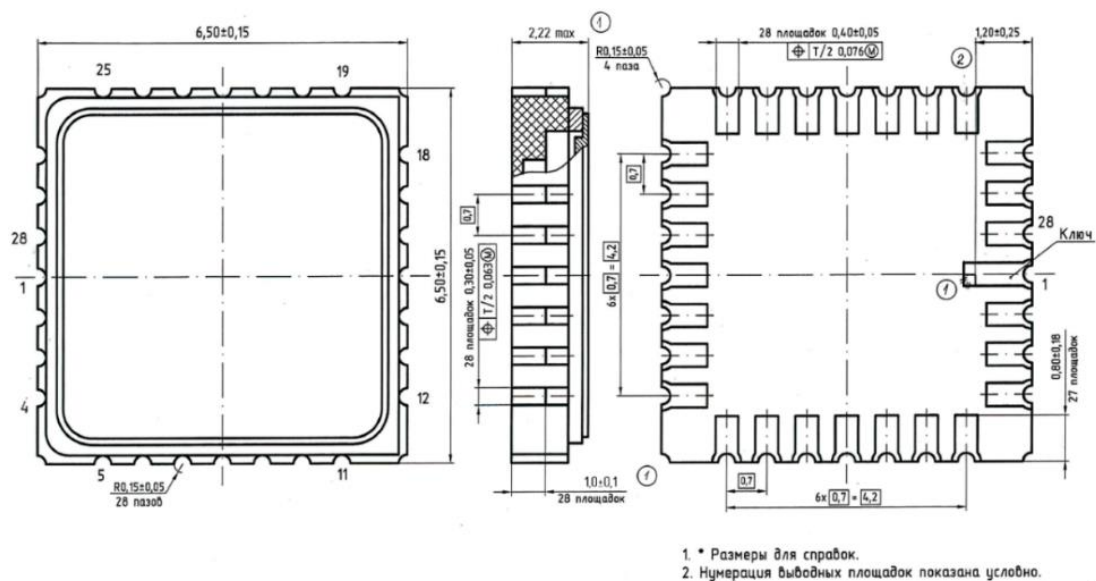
Габаритный чертёж корпуса МК 5123.28-1.01 (размеры в мм)
